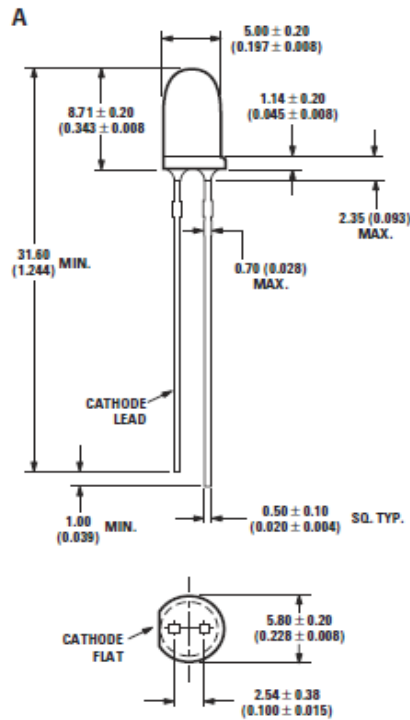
Dimensiones. (Datasheet HLMP-Exxx)
